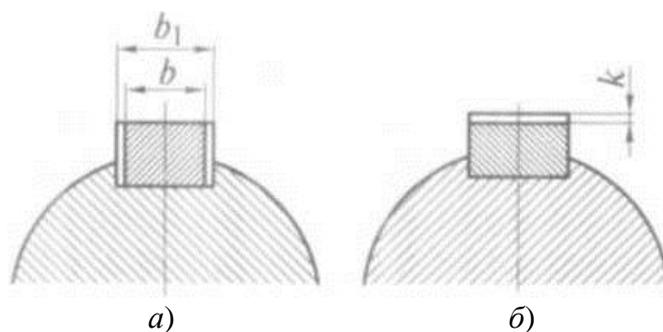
Соединения с клиновой (а) и призматической (б) шпонками
